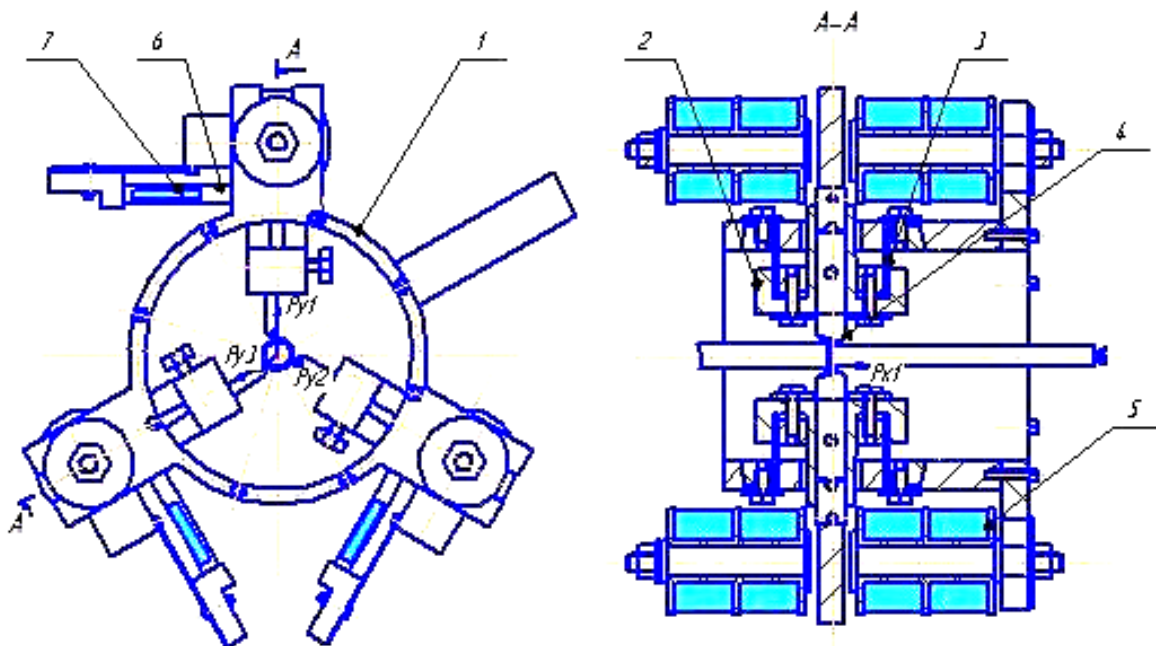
Схема конструкції багаторізевої головки із електромагнітними приводами
